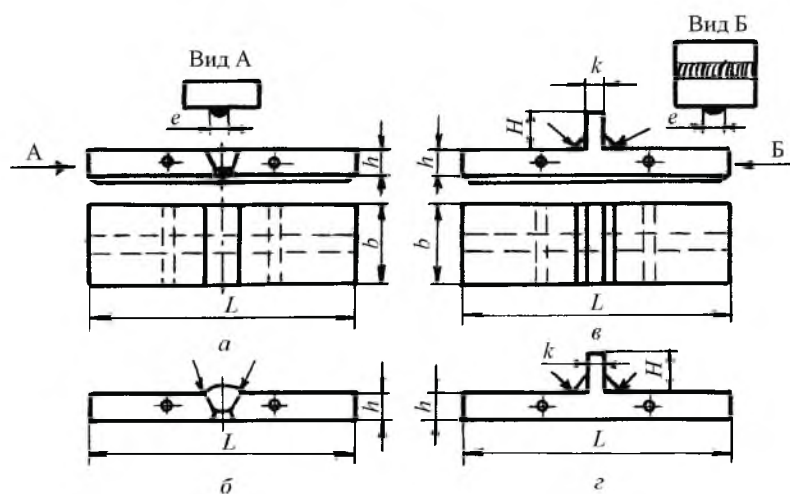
Типы сварных образцов для определения сопротивления усталости.
